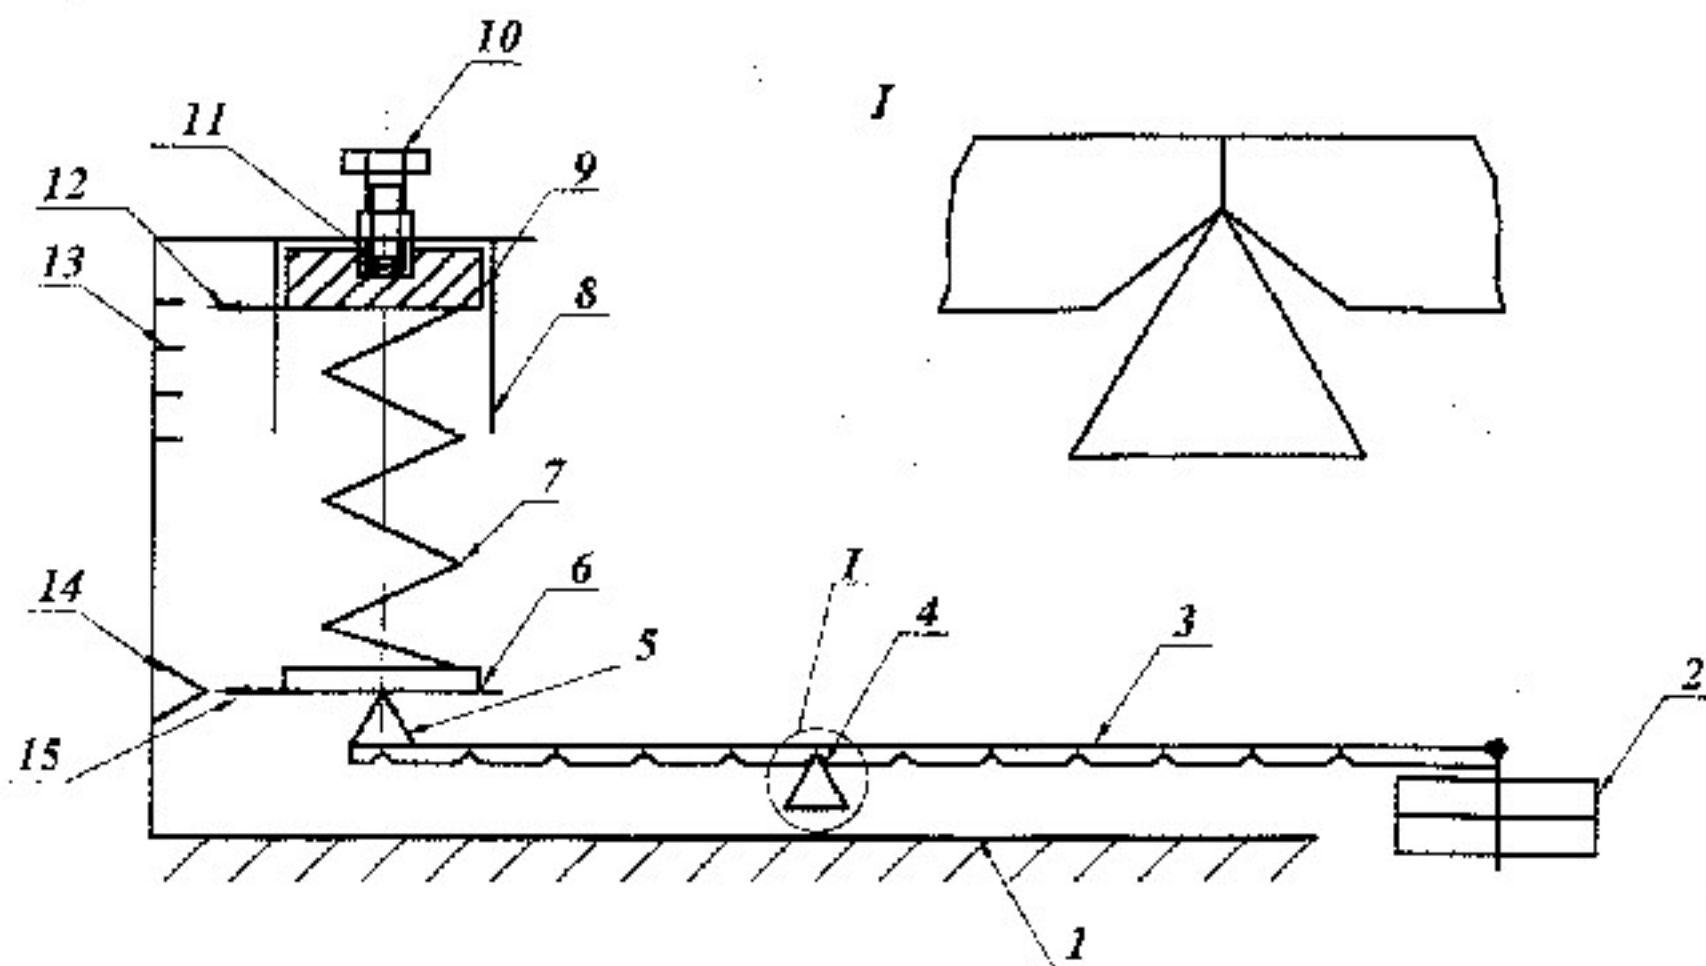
Предлагаемая схема приспособления для тарирования пружин
